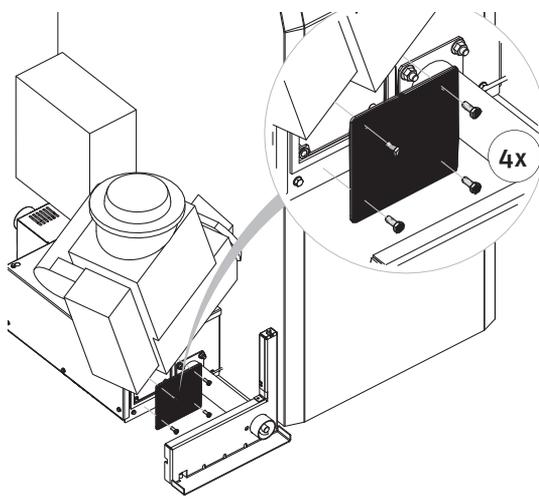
Retirer le couvercle et aspirer le contenu du cendrier
